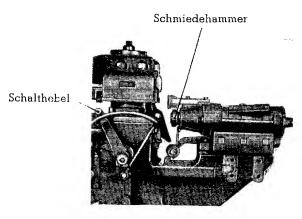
Maschine mit Schmiedehammer und Schalthebel, Lochhammer abgebaut
